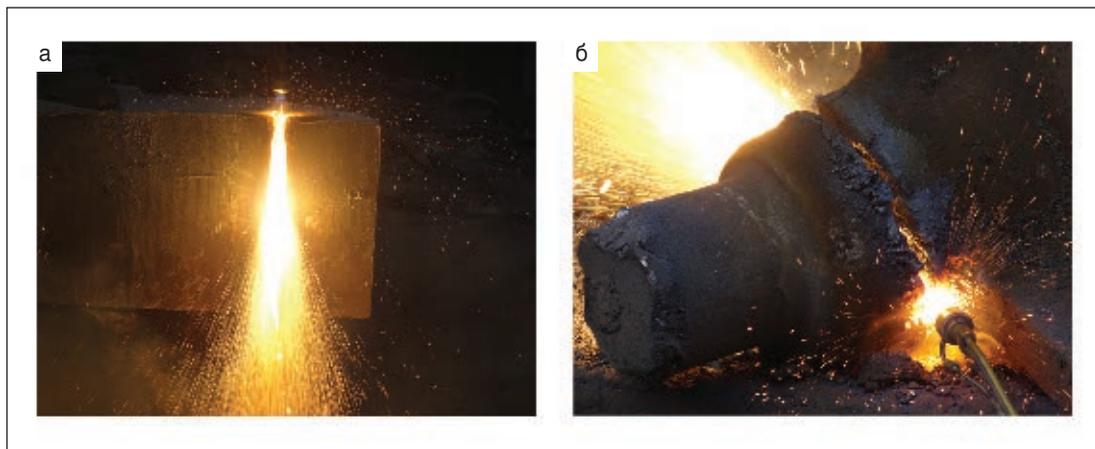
Резка образцов: а — сталь 95Х18 толщиной 450 мм; б — прибыль из серого чугуна диаметром 380 мм
